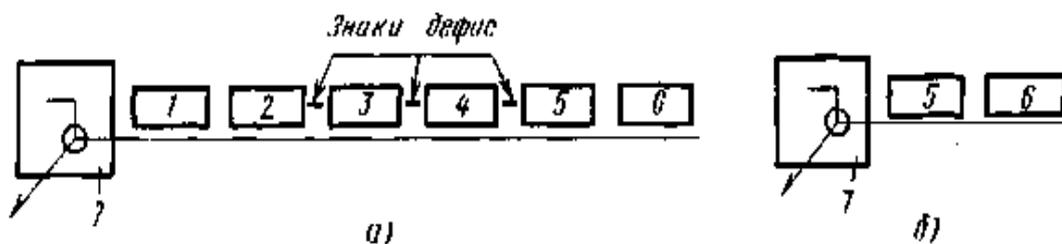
Структура обозначения сварного шва стандартного (а) и нестандартного (б)
